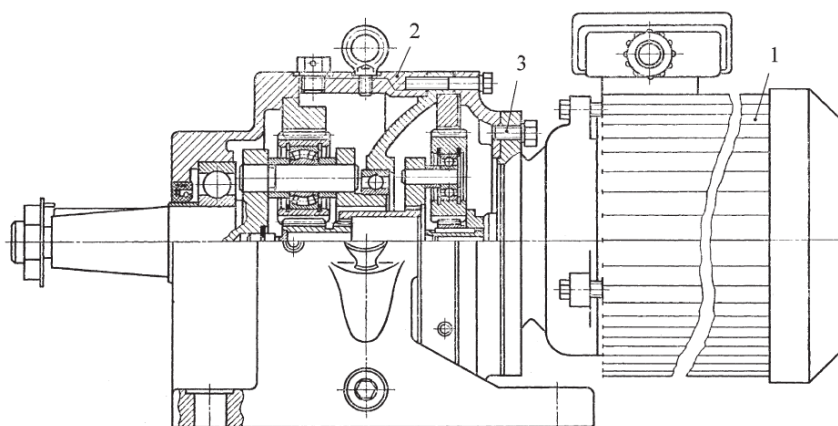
Планетарный двухступенчатый мотор-редуктор
